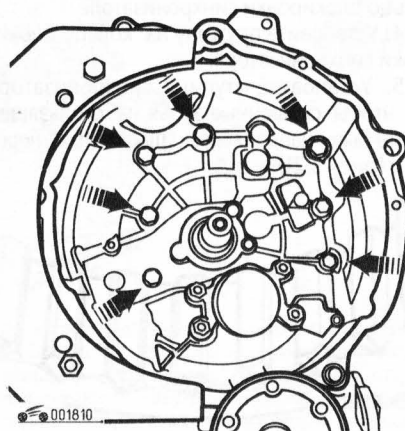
Расположение болтов крепления картера сцепления к картеру коробки передач
